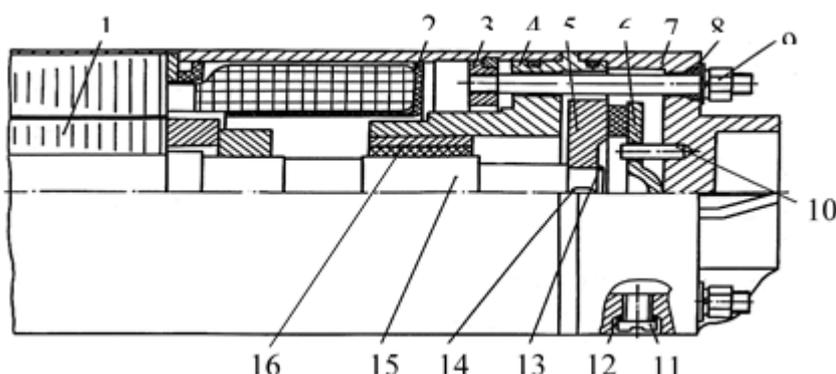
Электродвигатель погружной: 1 — статор; 2 — пескосбрасователь; 3 — основание; 4 — щит подшипниковый; 5 — пята; 6 — подпятник; 7 — днище; 8 — уплотнитель; 9 — гайка; 10 — штифт; 11 — болт; 12 — кольцо уплотнительное; 13 — кольцо пружинное; 14 — шпонка; 15 — ротор; 16 — подшипник резинометаллический
